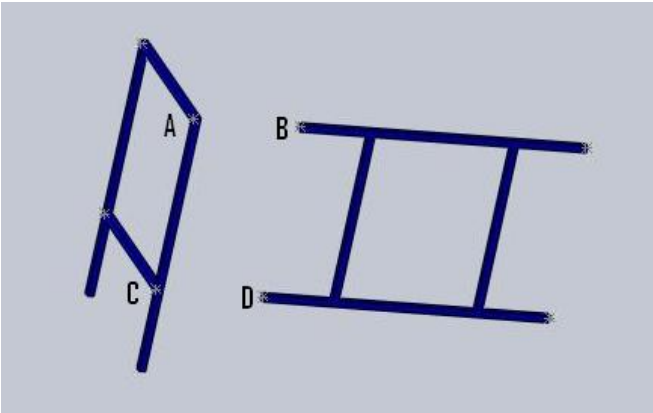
Ensamble de la parte lateral y frontal de la mesa
